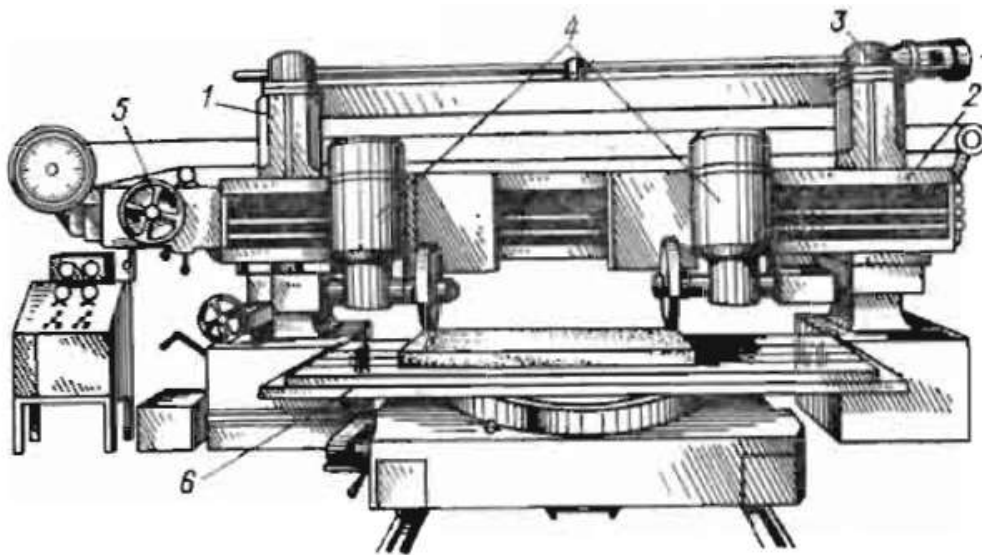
Окантовочно-фрезерний порталний верстат мод. МП-600 (фірма „Карл Майер“) [3]. Позначено: 1 – портал; 2 – траверса; 3 – механізм переміщення траверси; 4 – супорти; 5 – механізм переміщення супортів; 6 – поворотний стіл.
